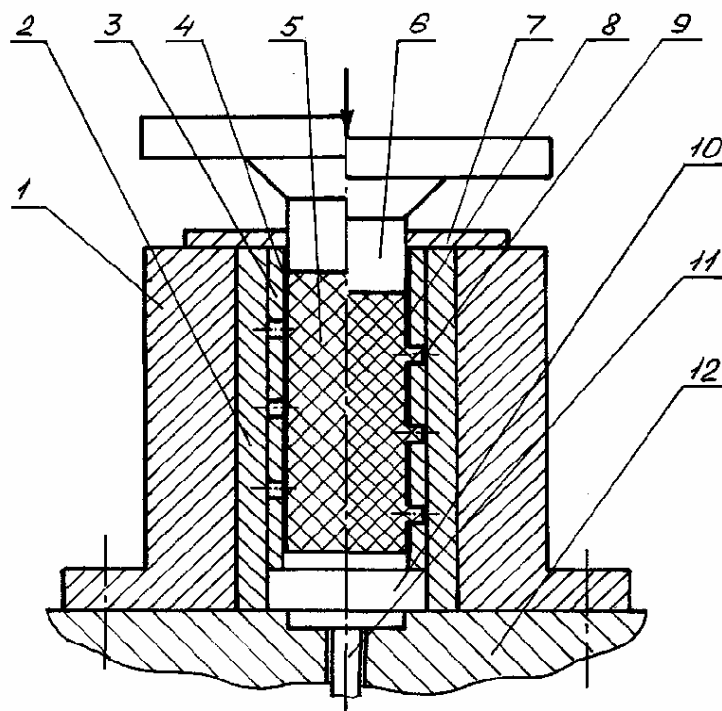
Схема штампа для пробивки отверстий в трубной заготовке полиуретановым пуансоном по жесткой матрице: 1 – обойма; 2 – вставка; 3 – матрица; 4 – трубная заготовка; 5 – пуансон; 6 – шток; 7 – направляющая; 8 – деталь; 9 – отход; 10 – упор; 11 – выталкиватель; 12 – стол пресса
